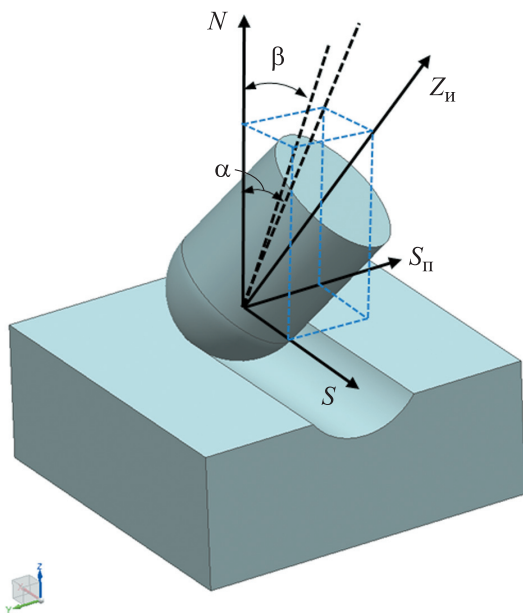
Схема относительного положения инструмента и заготовки с углами наклона α и опережения β :
